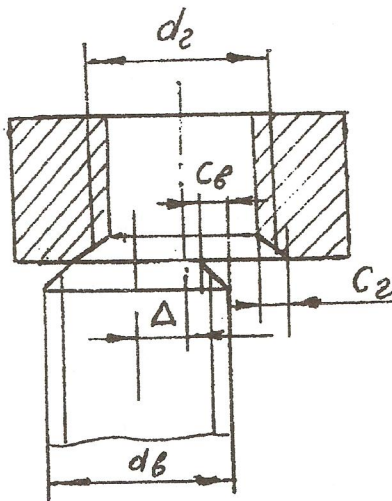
Схема сборки деталей, сопрягаемых по резьбовым поверхностям
